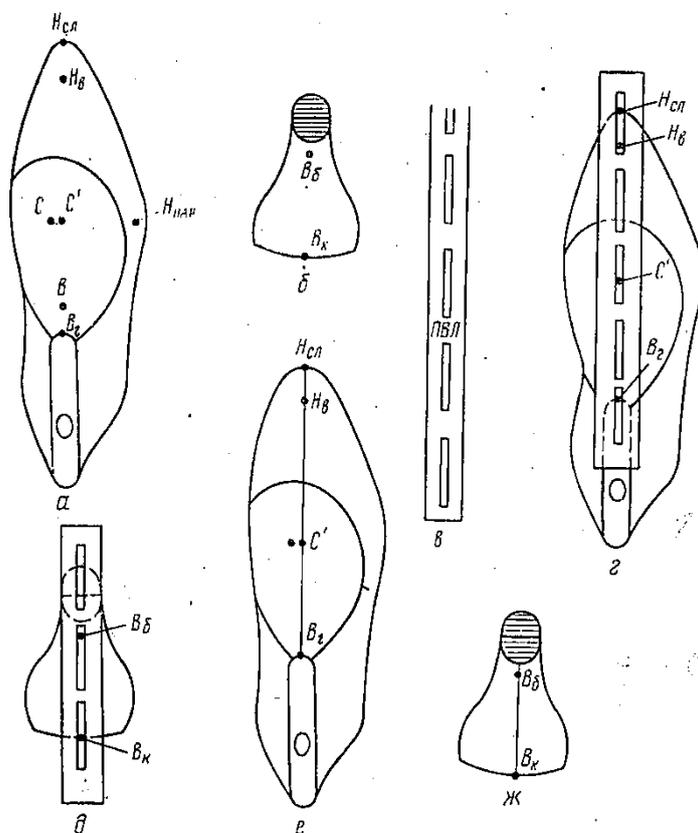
Этапы подготовки колодки к получению условной развертки боковой поверхности колодки
